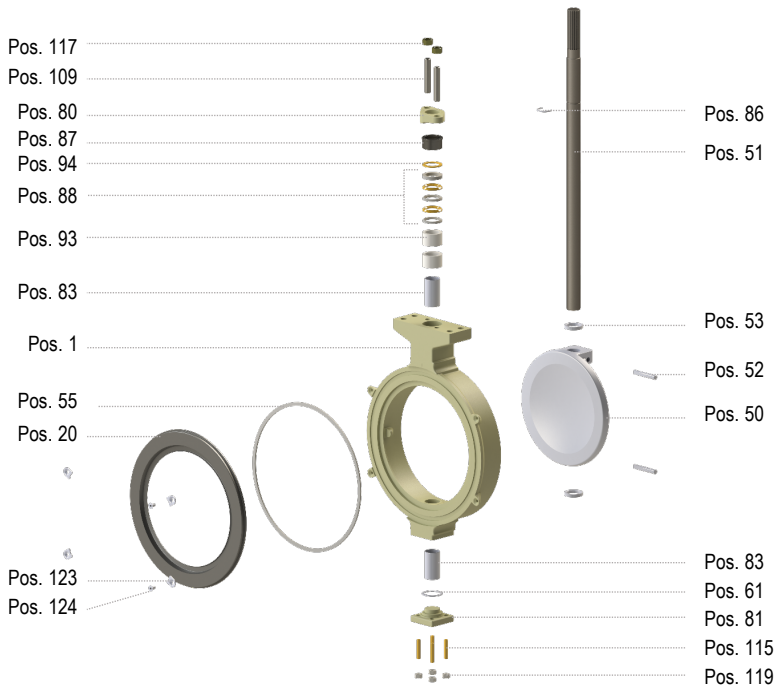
Explosionszeichnung eines Ventils in Zwischenflanschausführung.
